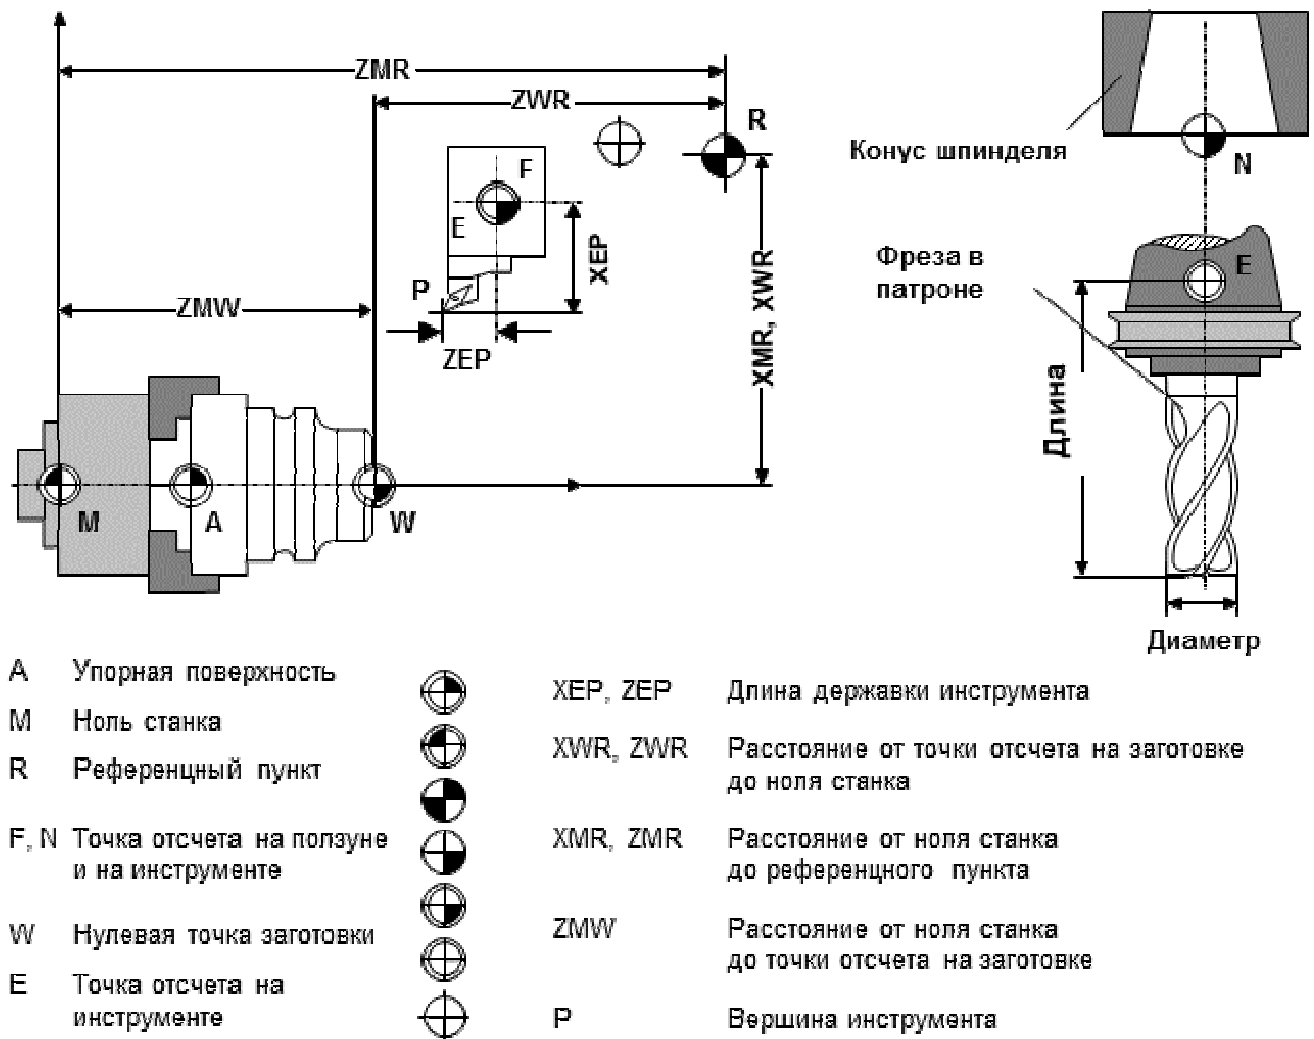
Контрольные точки токарного станка с ЧПУ и фрезерного инструмента
